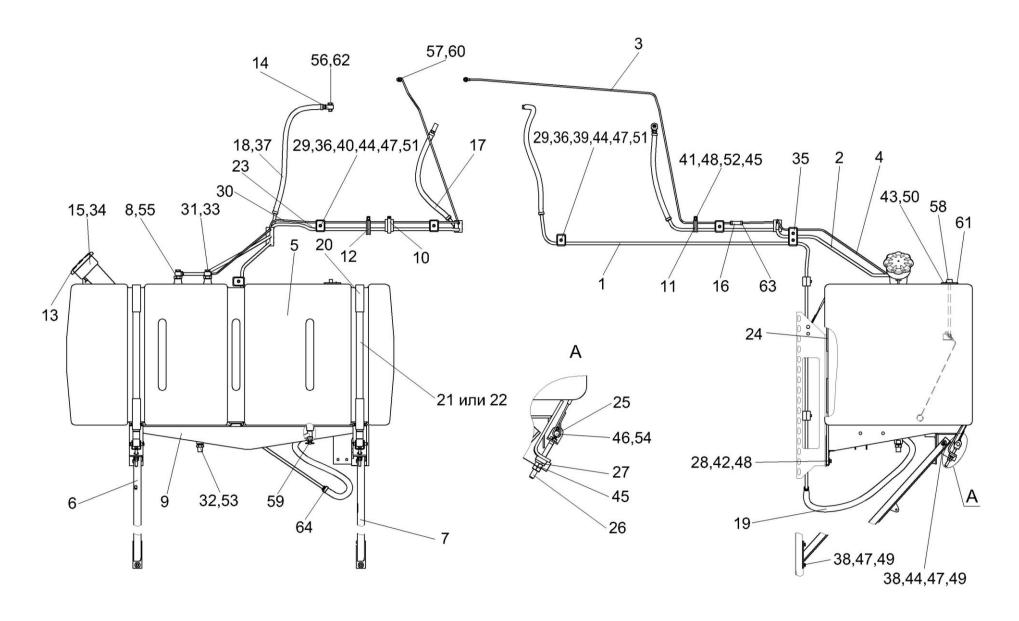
Установка бака топливного КЗК-10-1-0126000
